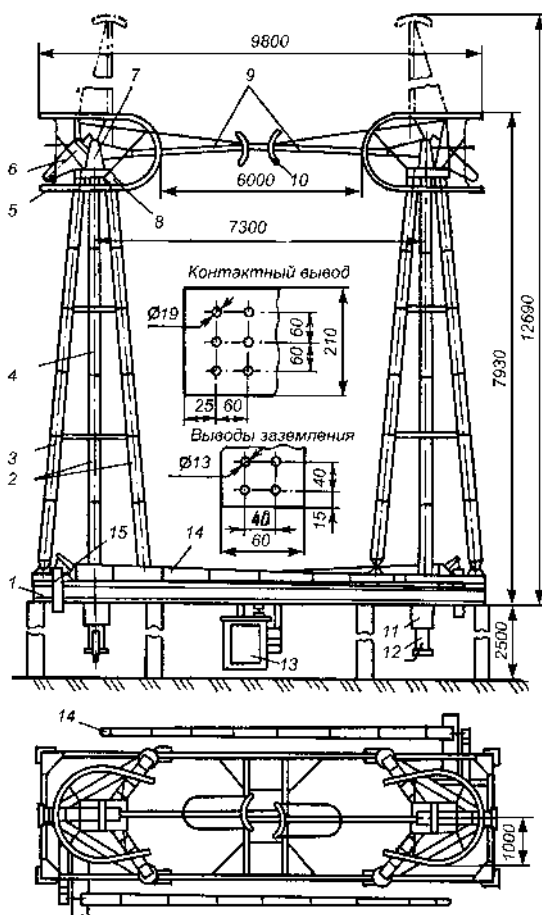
Разъединитель типа РНВЗ-750П/4000У1:
